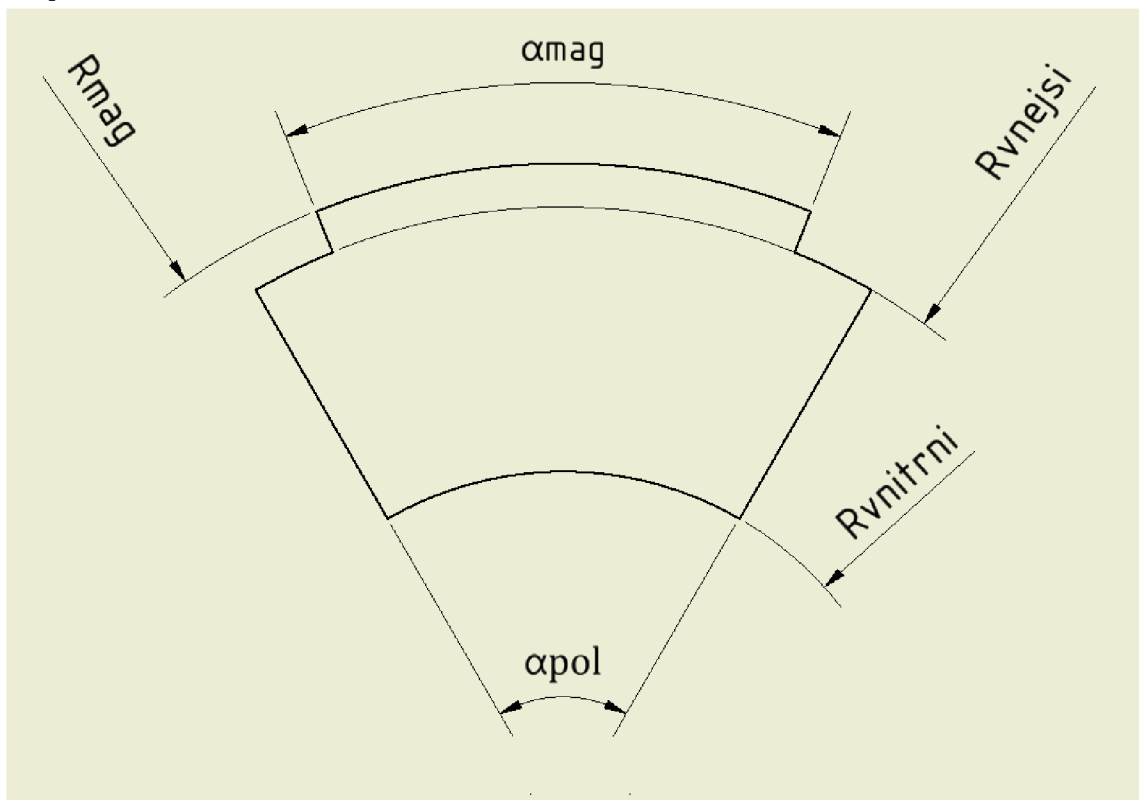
3 Náčrt rotoru s vnořenými magnety
